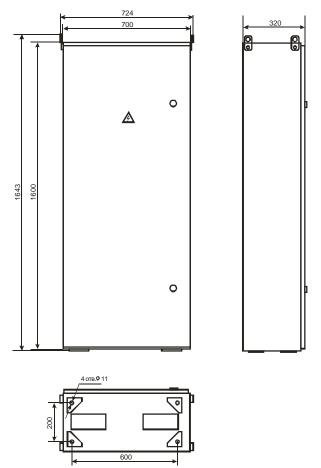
Внешний вид, габаритные и установочные размеры корпуса шкафа силового ШРС1-XX-7-Узола.
